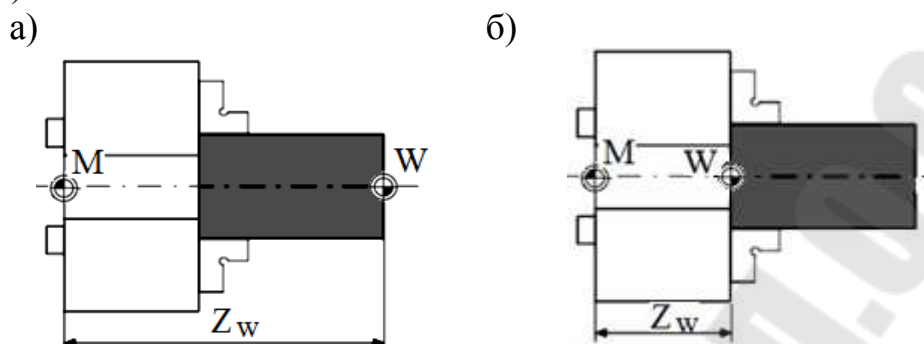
Схема установки нулевой точки заготовки на токарном станке с ЧПУ
